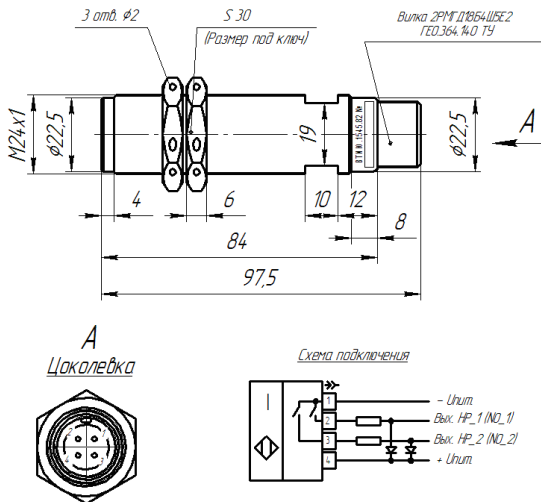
Габаритный чертеж и схема подключения ВТИЮ.1545.82
